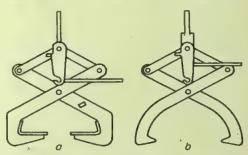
a Profilstahlzange, b Holzstammzange
